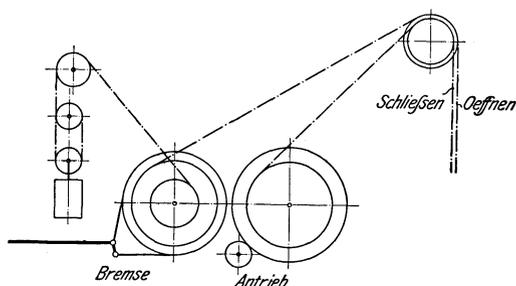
Greiferwinde mit Gegengewichtsantrieb für die Entleertrommel.
